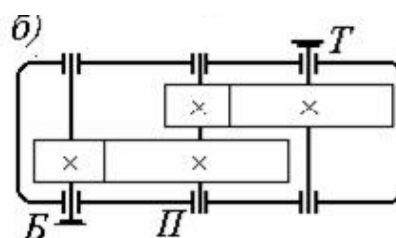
Кинематическая схема двухступенчатой зубчатой передачи
